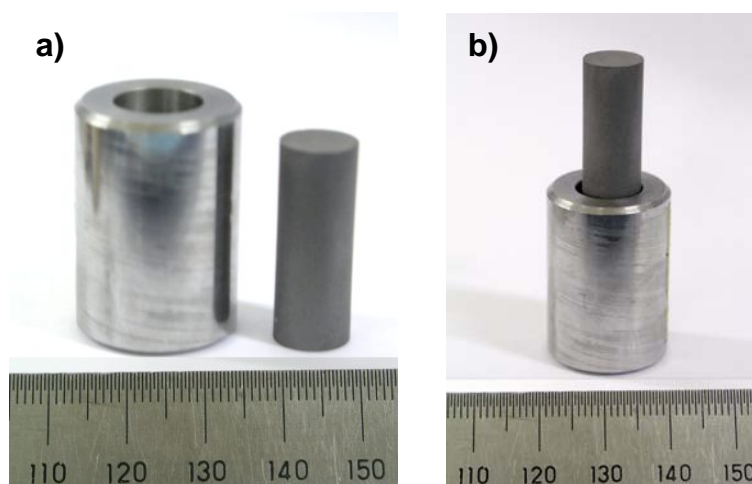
(a) Probetas utilizadas en el estudio (b) Disposición de las probetas para el ensayo de soldadura por difusión.
